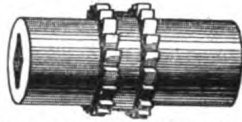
Stednuß zum „Rapid“-Schraubenschlüssel für tiefliegende Muttern.
